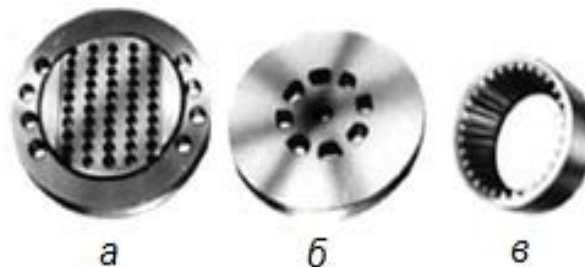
Зразки виробів: а – сідло клапана компресора; б – магнітопровід ротора; в – муфта внутрішнього зчеплення
